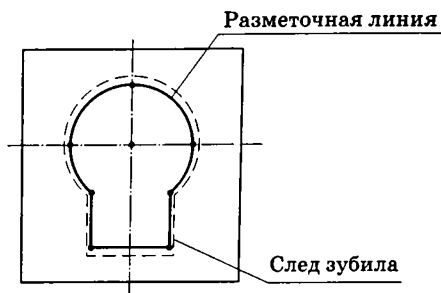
Разметка заготовки из листового металла при рубке на плите
